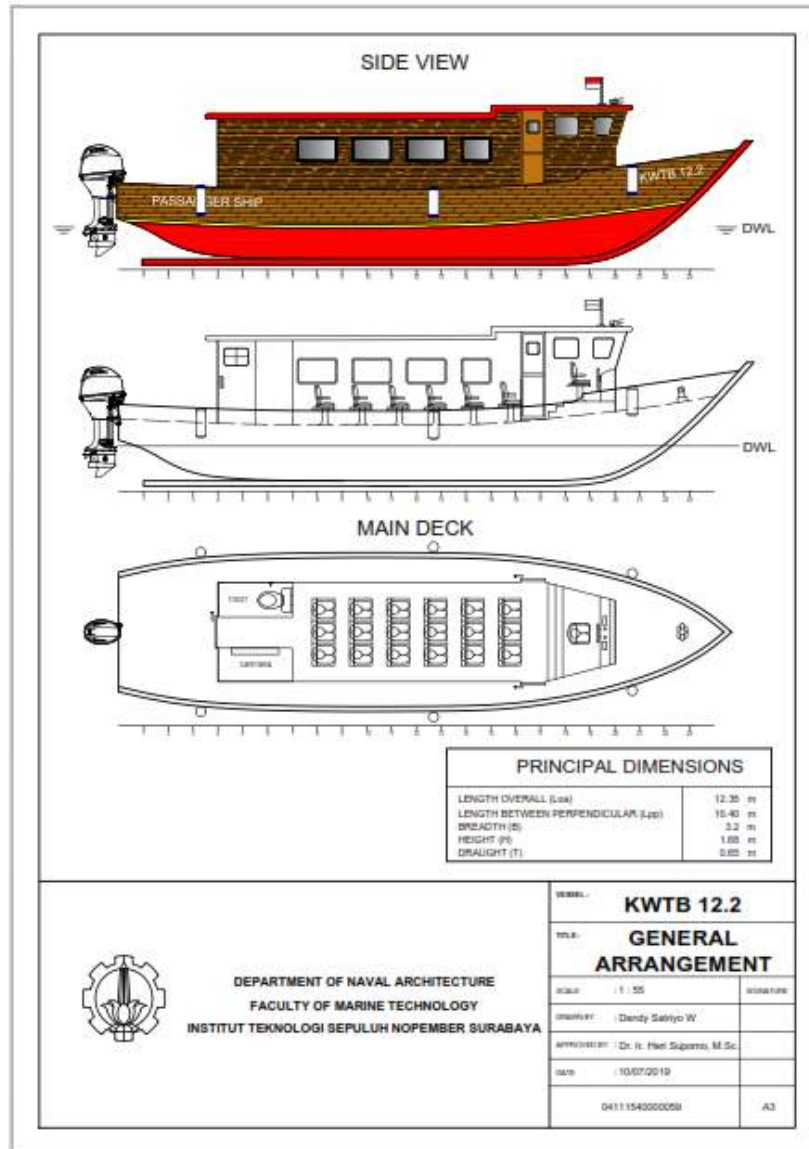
Rencana umum (*general arrangement*) kapal wisata pancing 12 m
